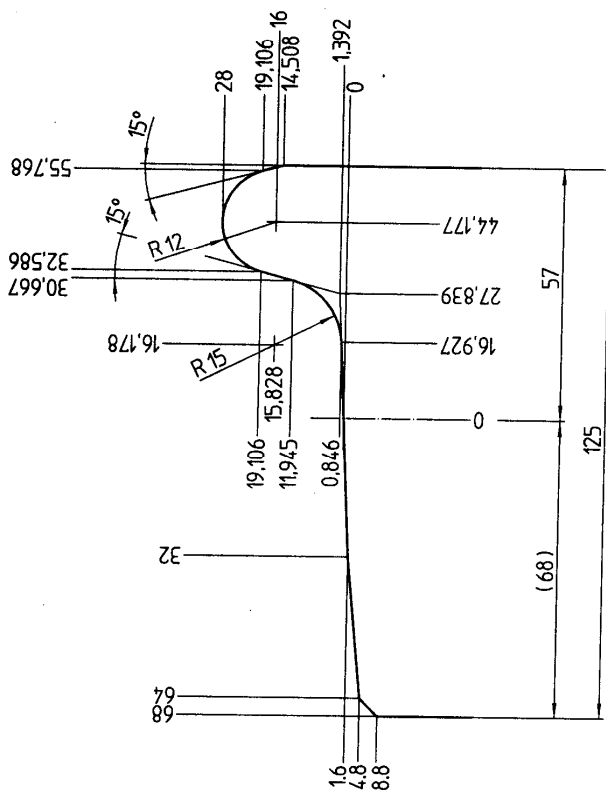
Рабочий чертеж колеса Ø 750 мм
